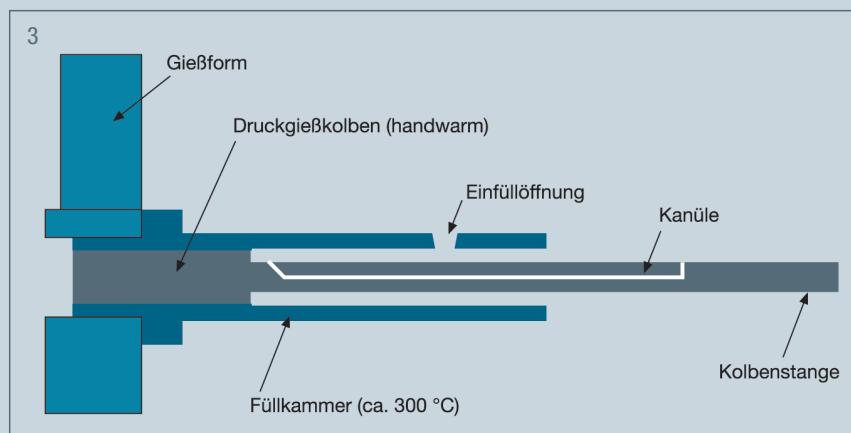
Der wässrige Kolbenschmierstoff „Enviro 781“ wird mit einer feinen Kanüle, die sich in einem geprästen Schlitz der Kolbenstange befindet, vom Hydraulikzylinder herkommend bis zu dem eingeschraubten Kolben geführt.
